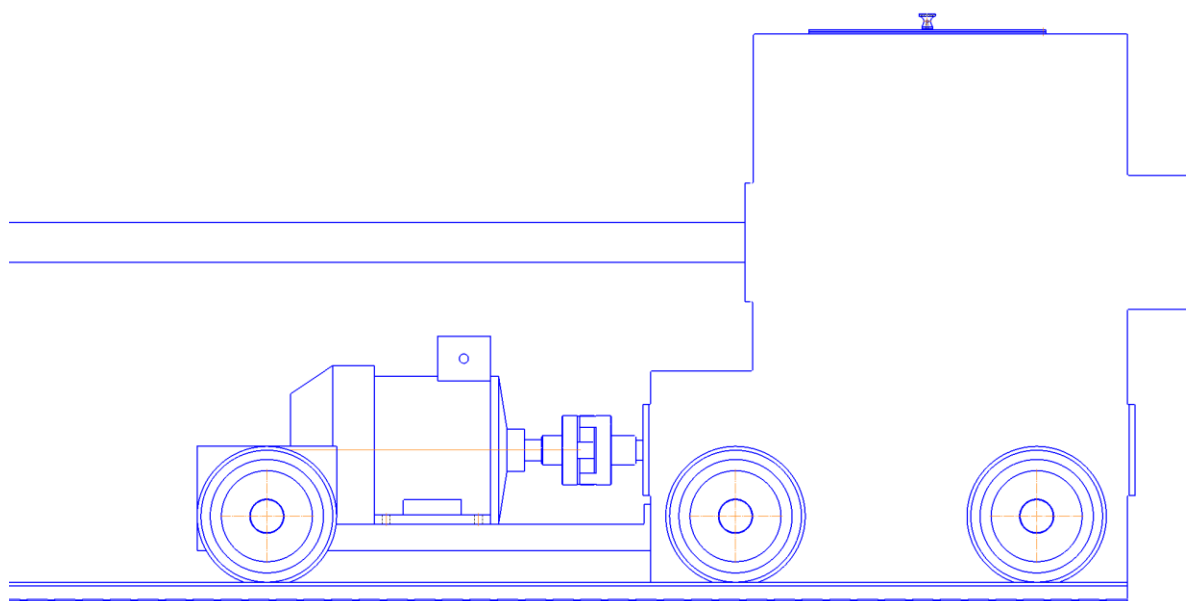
Чертёж тележки плазмотрона (вид сбоку)
